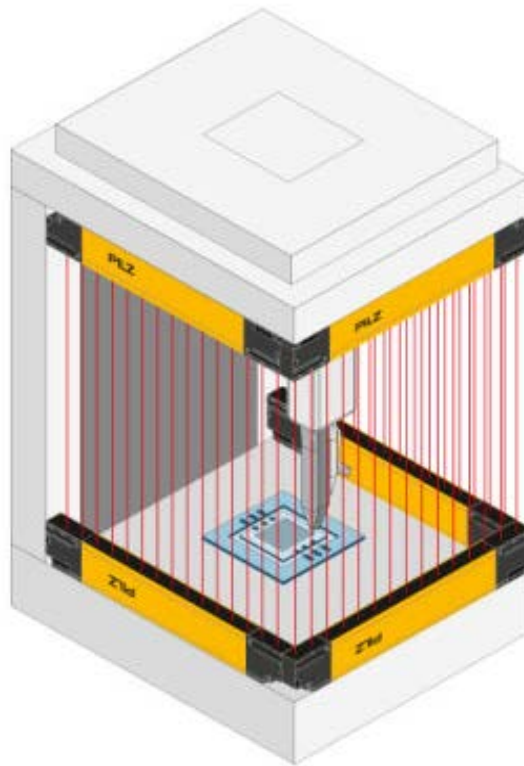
Exemplo de aplicação de uma barreira imaterial PILZ (PILZ, 2018)
